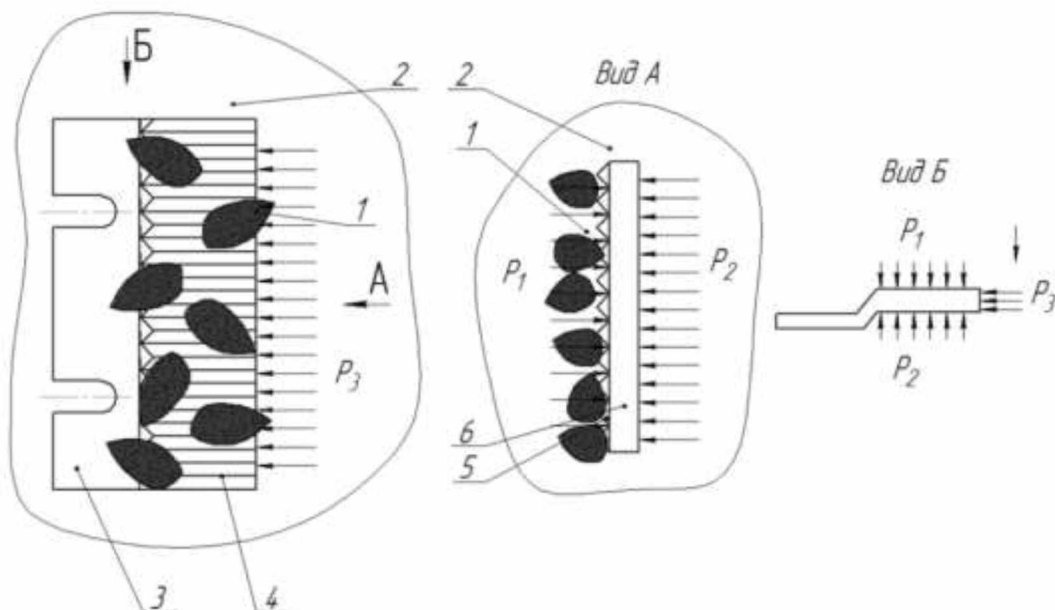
Процес взаємодії коренеплоду з ножом при подрібненні: 1 - подрібнюючий буряк; 2 - нерухомий циліндр установки; 3 - привалочна зовнішня площину ножа; 4 - межі ножа; 5 - ріжучі кромки ножа; 6 - порожнина сходу стружки
